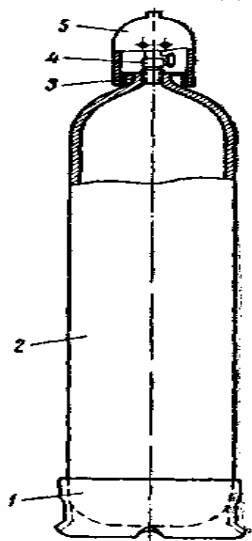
Балон для кисню: 1 — башмак; 2 - корпус; 3 — кільце; 4 - вентиль; 5 - ковпак.
